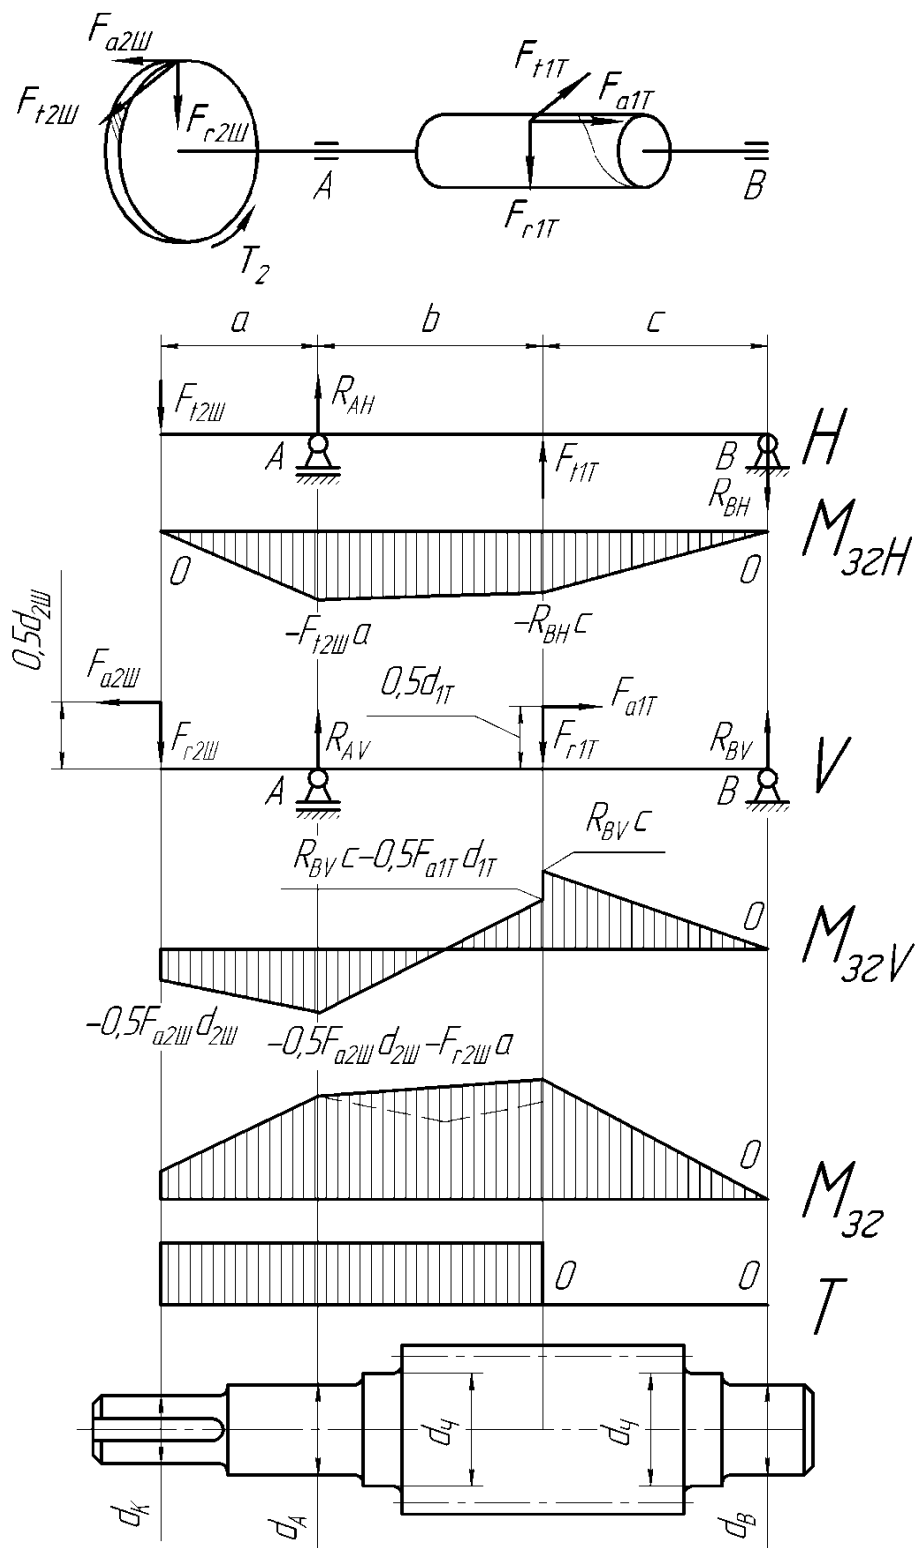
Розрахункові схеми, епюри згинальних і обертаючого моментів та ескіз проміжного вала циліндрично-черв'ячного редуктора
